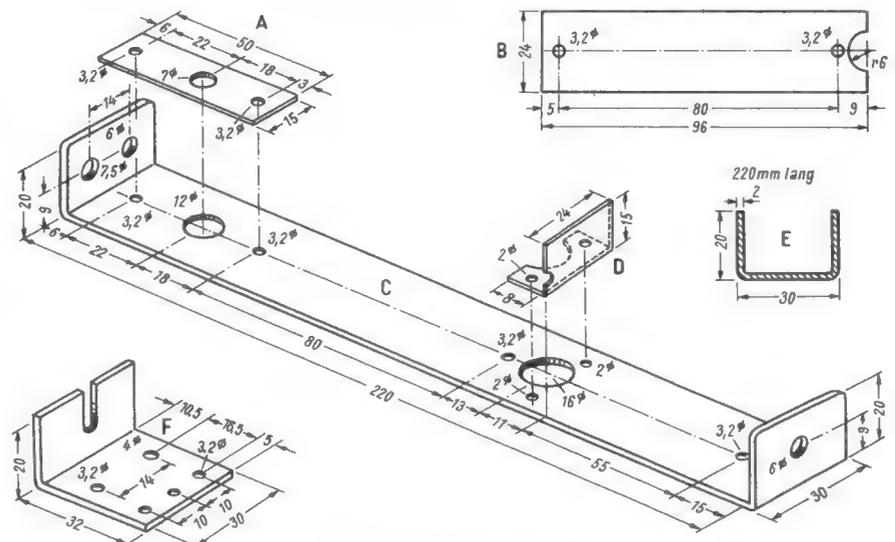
Die mechanischen Bauteile. A = Messing- oder Aluminiumblech 1 mm; B = Isolierplatte; C = Aluminiumblech halbhart 2 mm; D = Aluminium 1 mm; E = Aluminiumprofil; F = Aluminiumblech halbhart 2 mm
